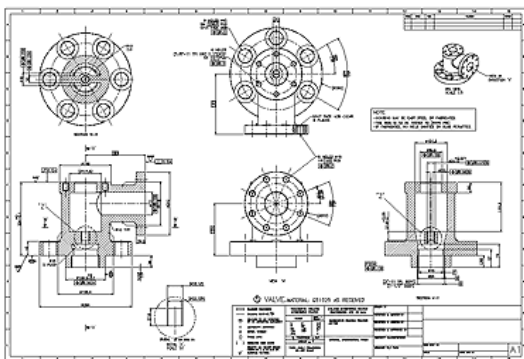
Especificação GD&T do Produto indicada em desenhos 2D
